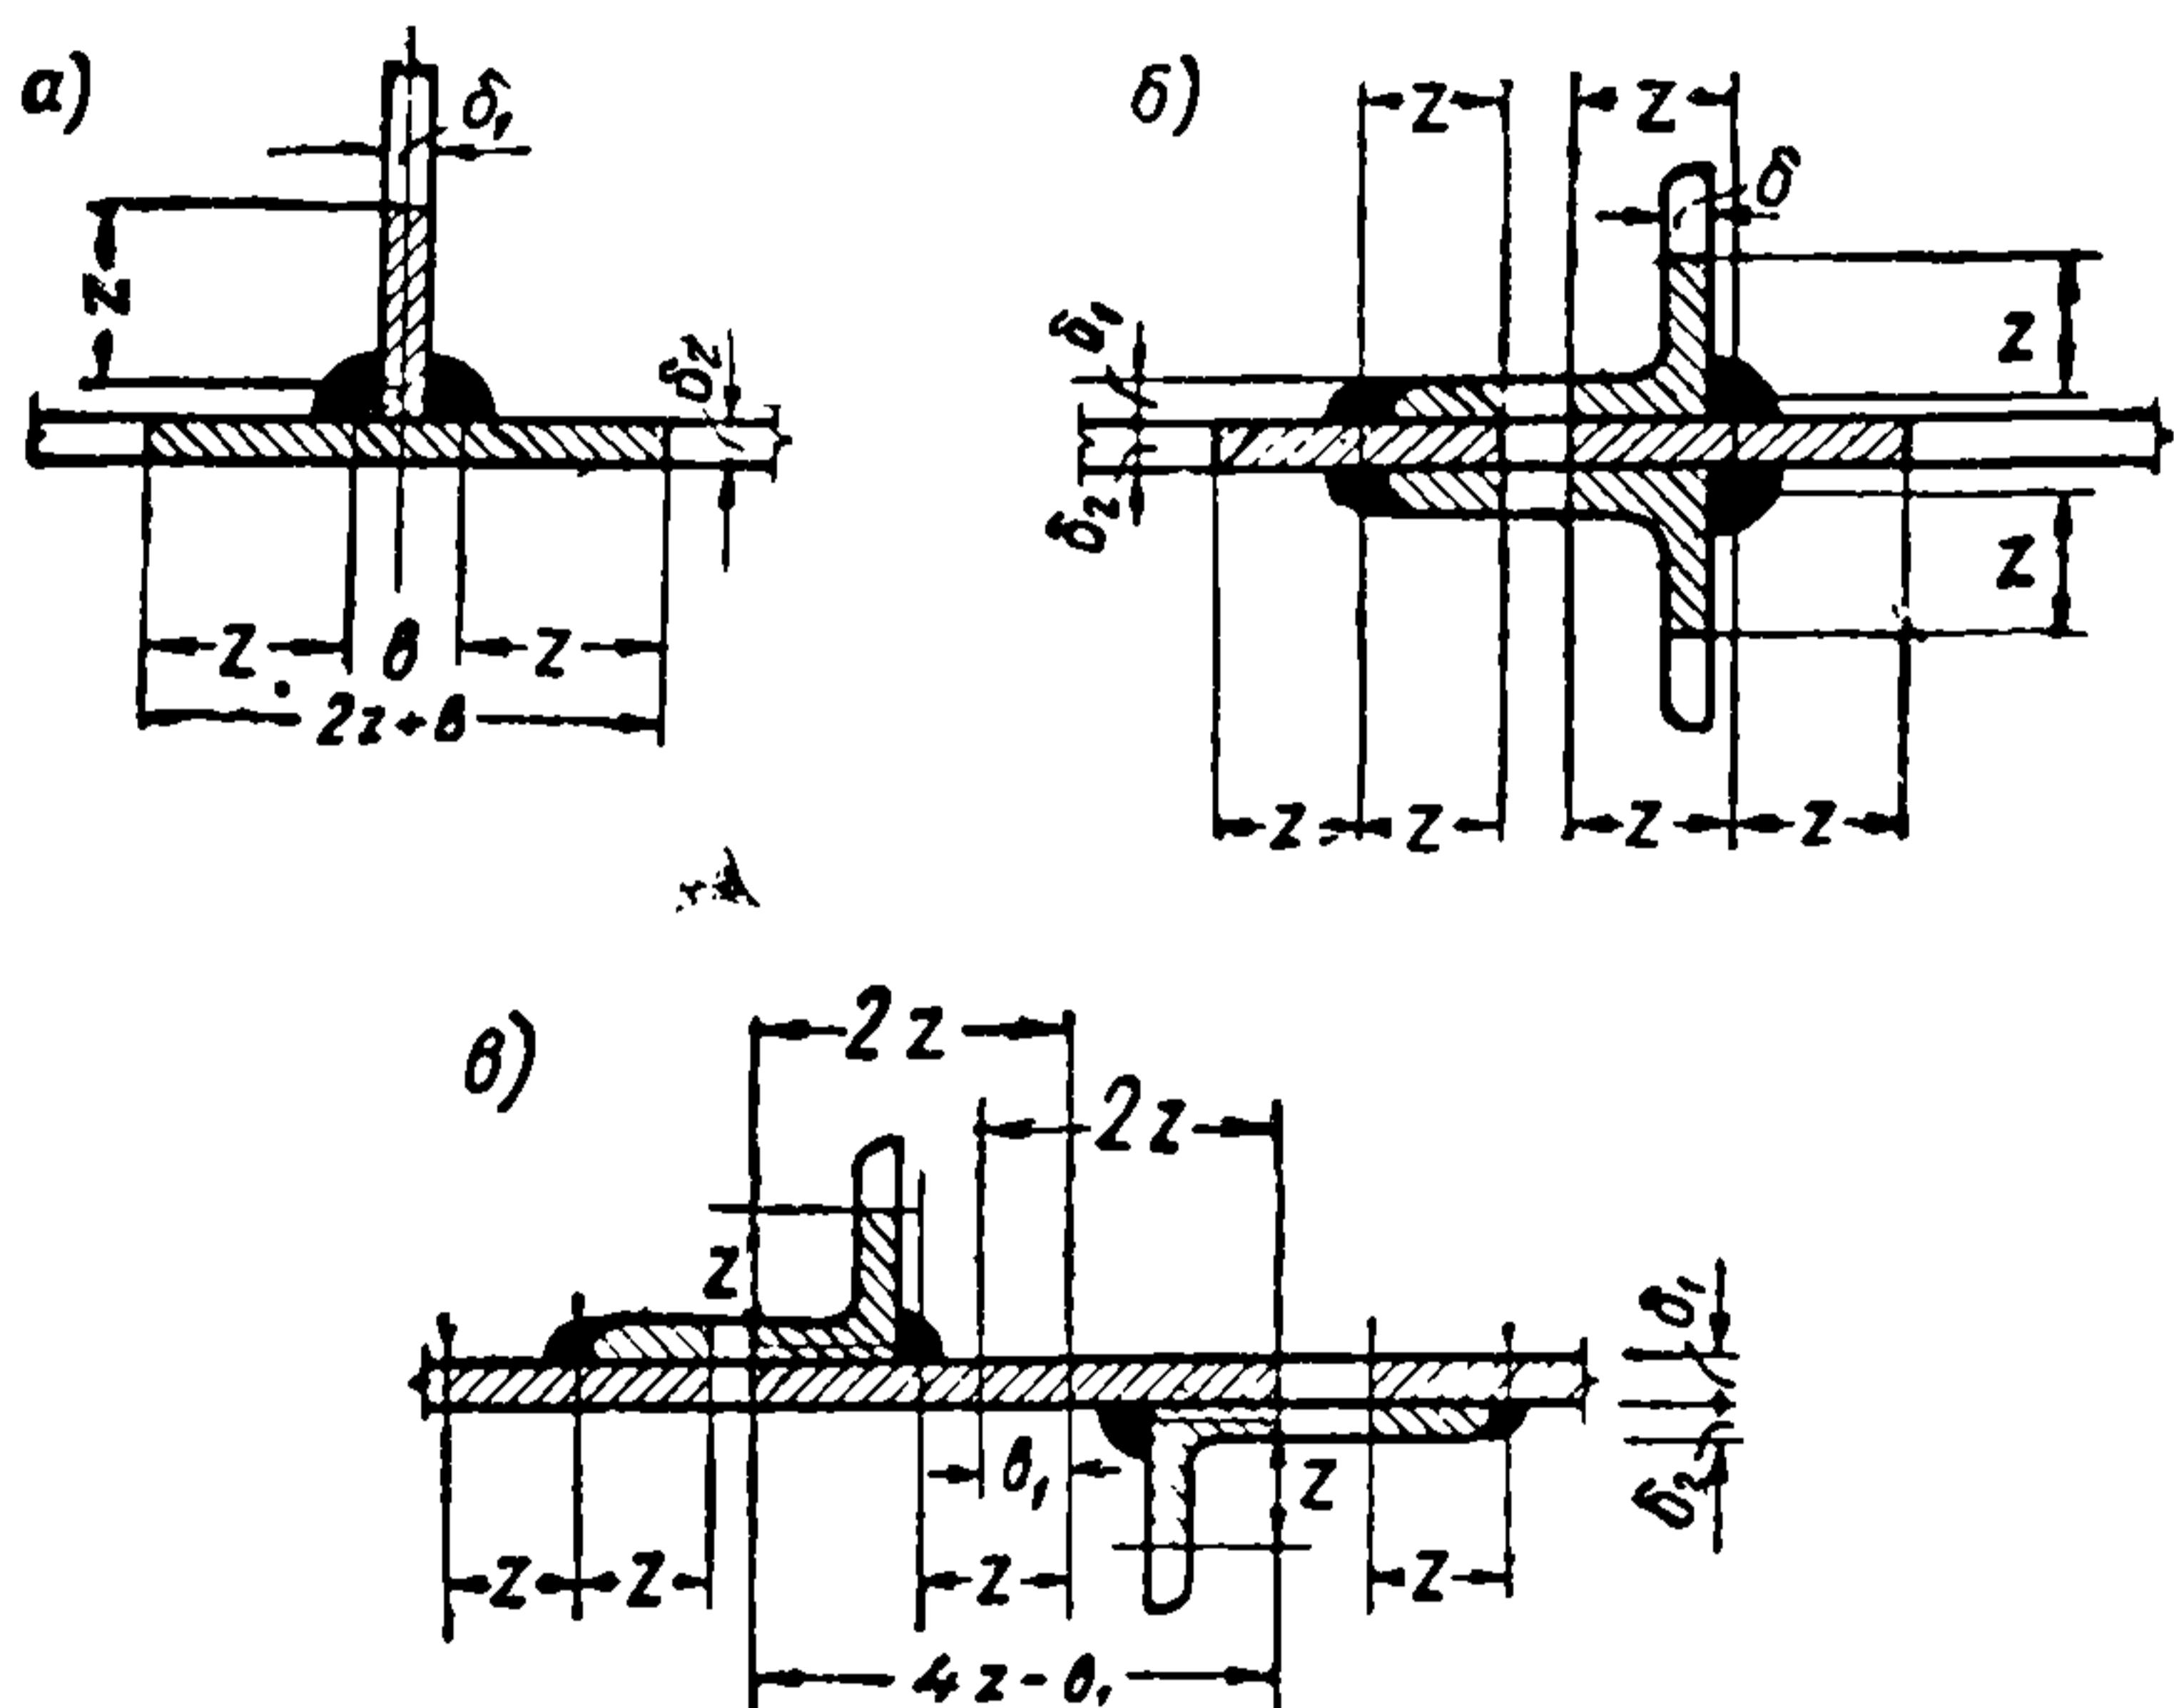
Схемы определения зон термического влияния в соединениях с угловыми и фланговыми сварными швами
